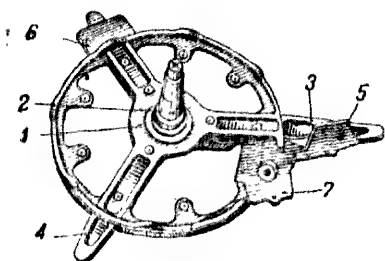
Литая опора (крестовина) с запрессованным штырём:
